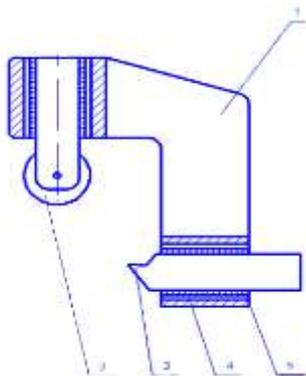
Комбинированный инструмент в форме скобы – двухполюсника: 1 – скоба-двухполюсник; 2 – ролик-электрод; 3 – резец – электрод; 4 – электромагнитные катушки; 5 – консталин
